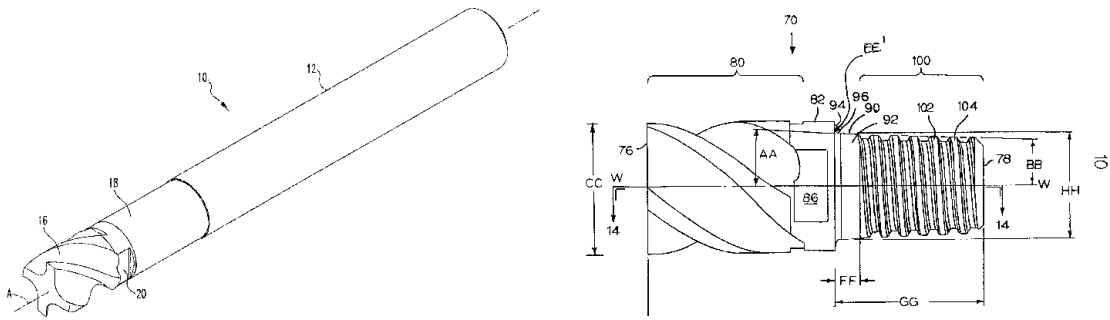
Зчіпний механізм для різального інструменту (Modular tool interface (Duo-Lock)) [7]
